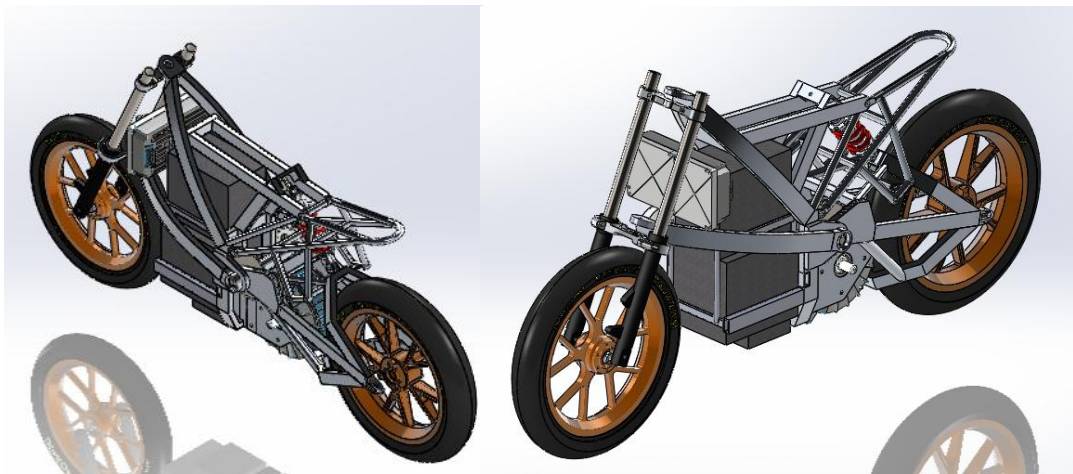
Conjunto final con elementos accesorios, suspensiones, motor y baterías⁹¹
